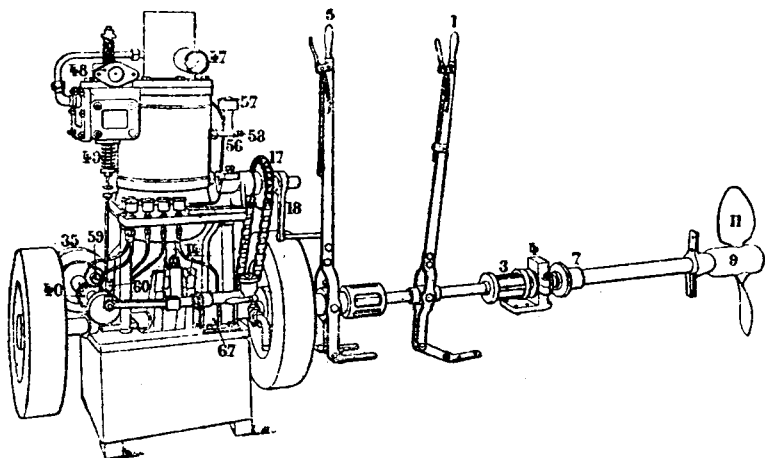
Пускъ въ ходъ двигателя посредствомъ рукоятки 18 и цѣпи 17, идущей по зубчаткѣ на добавочной оси. — 1, рычагъ перестановки лопастей 11 на втулкѣ 9. — 3, упорный шариковый подшипникъ съ направляющимъ подшипникомъ 4 и набивкой 7. — 5, рычагъ сцѣпленія. — 17, накаленный шаръ, производящій вспышку, помѣщенный въ кожухъ. — 48, всасывающій и выпускной клапаны. — 56, 57 и 58, клапанъ, масленка и колпачекъ для смазки цилиндра. — 35, центробѣжный регуляторъ. — 40, кулачекъ выпускного клапана. — 59, роликъ для подъема выпускного клапана. — 14, колѣнчатый валъ. — 67, водяной насосъ. — 60, масленка на шатунѣ насоса.
